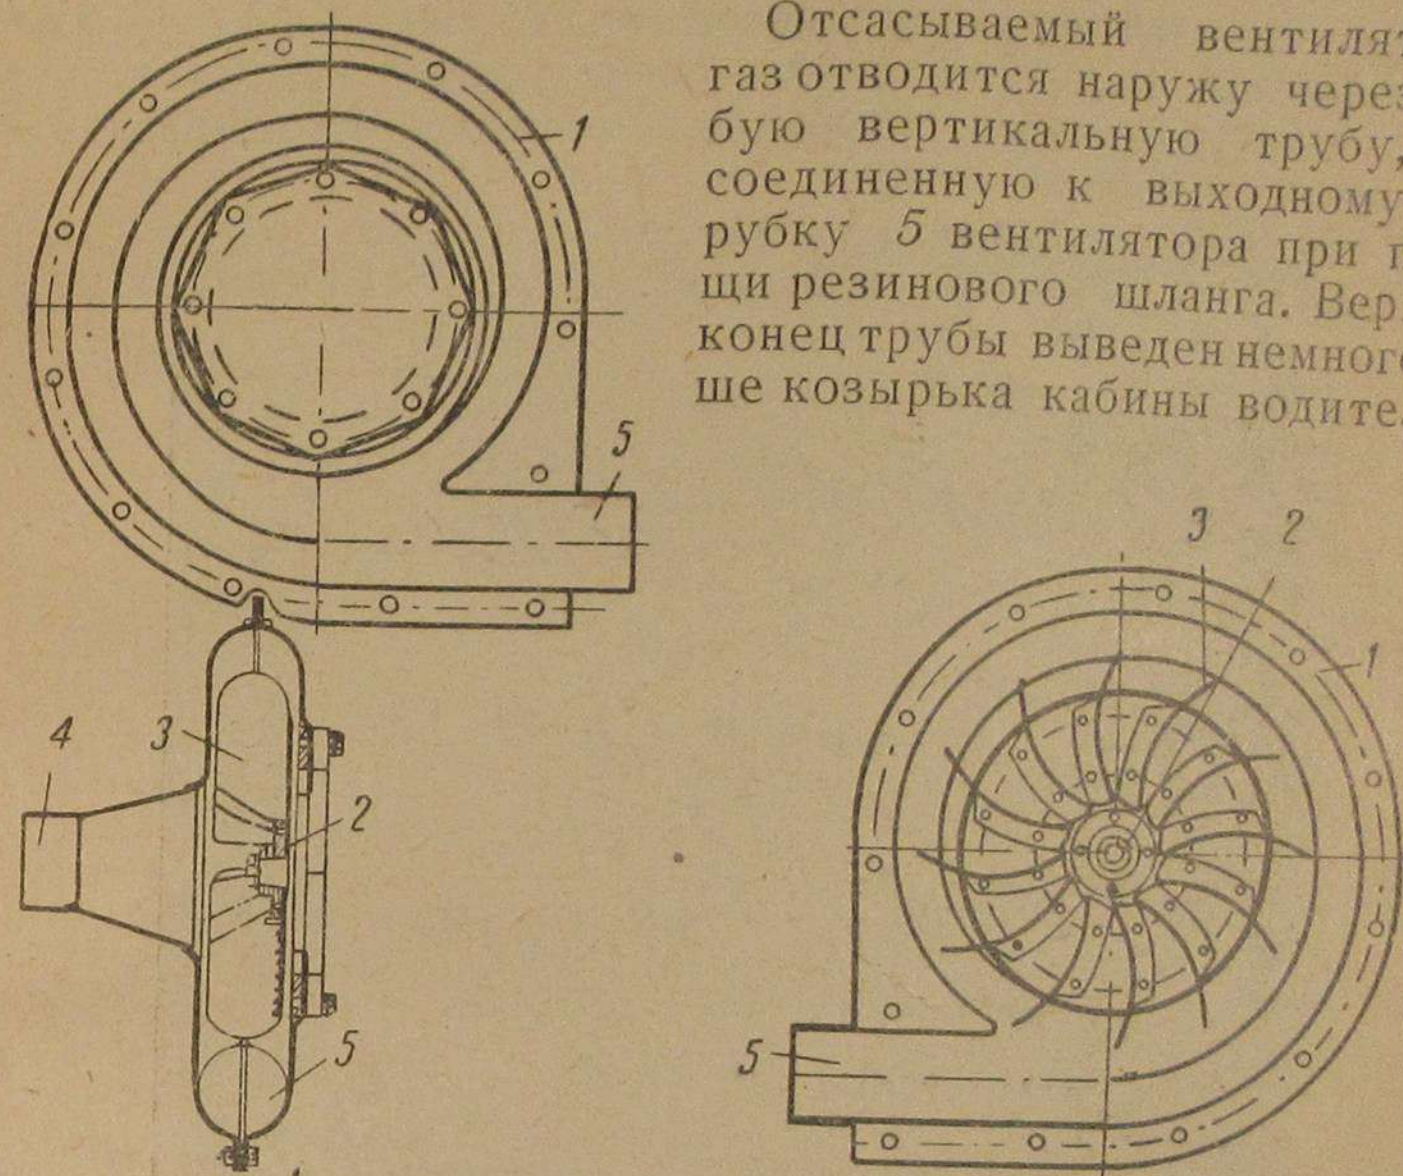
Раздувочный центробежный вентилятор установки ЗИС-21:
